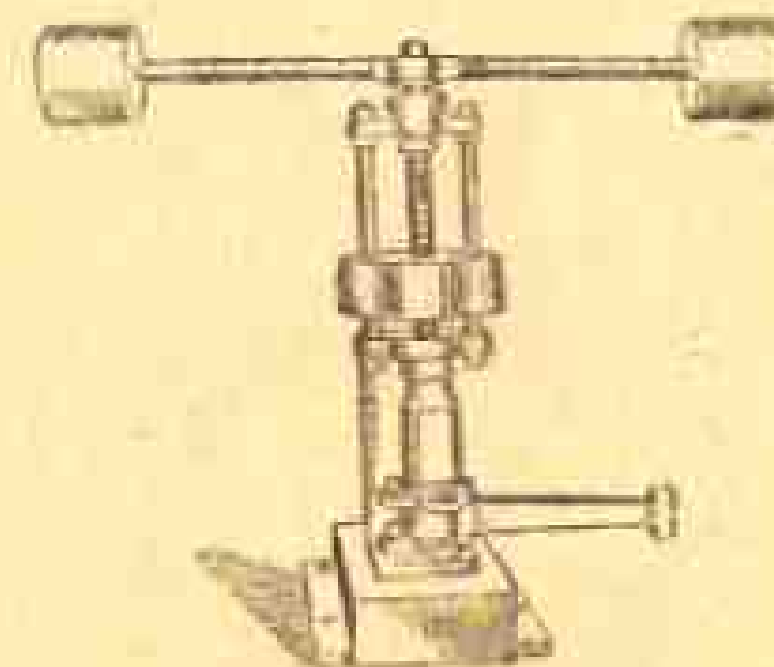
Выпрессовка фиксирующей втулки главного шатуна
